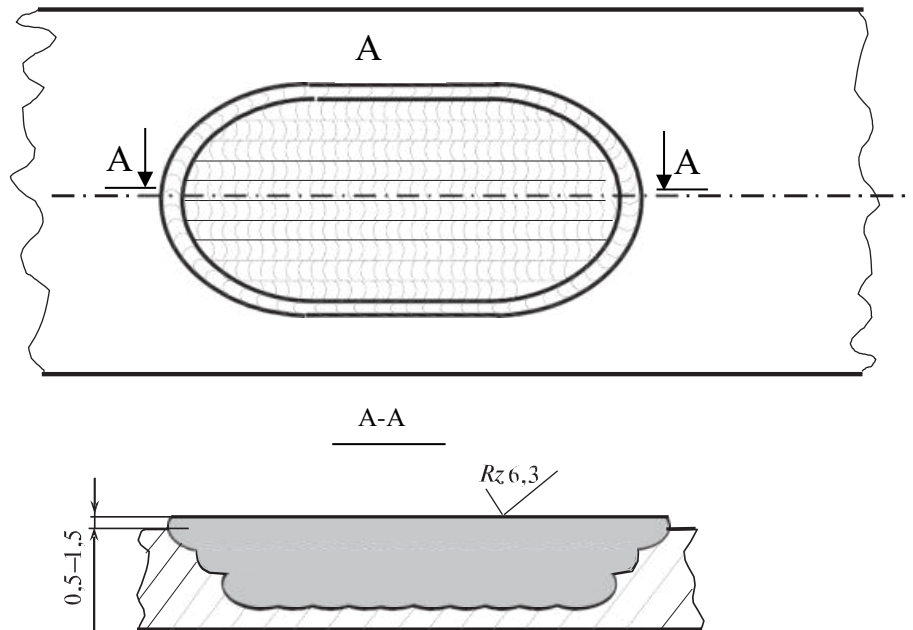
Дефектный участок, отремонтированный сваркой (наплавкой)
